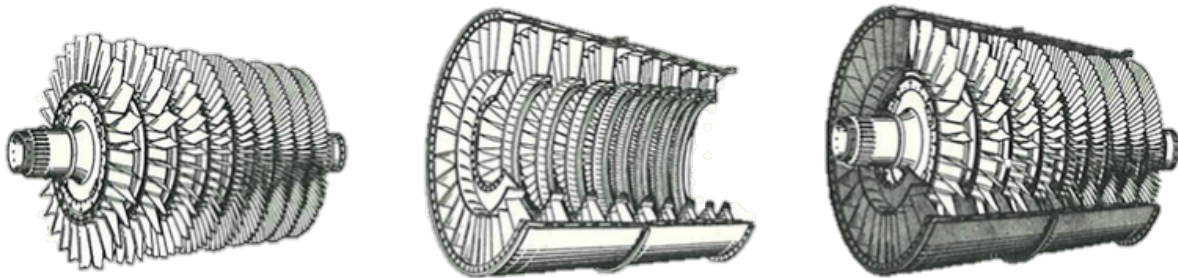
Rotor (1), Estator (2) e montagem (3) de um compressor axial [4].
